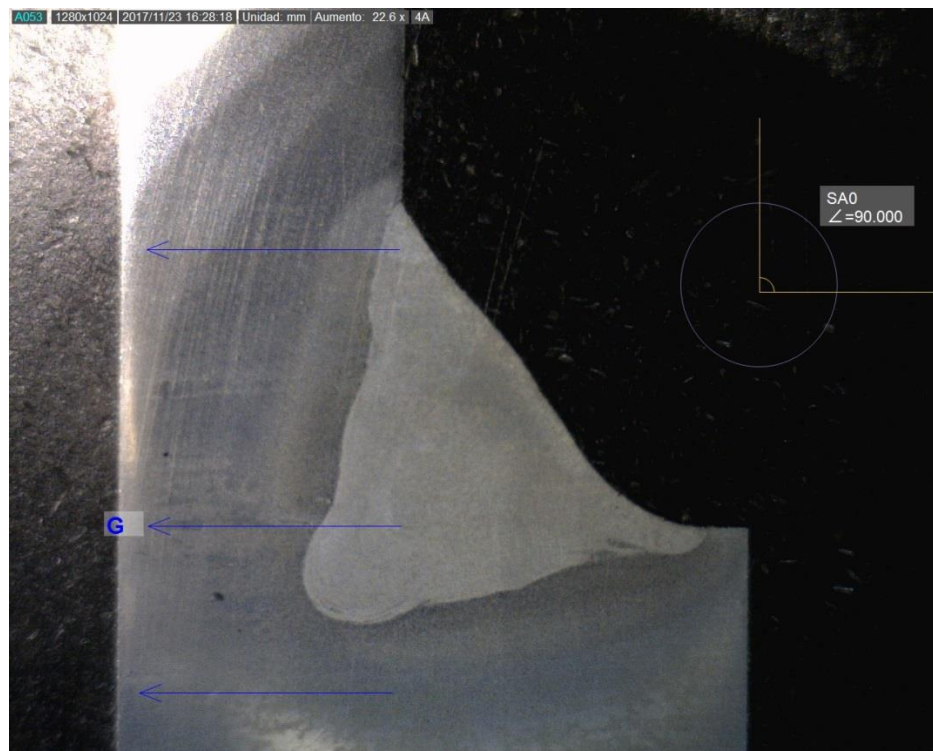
8 Perfil obtenido en cupón de soldadura 4B.
